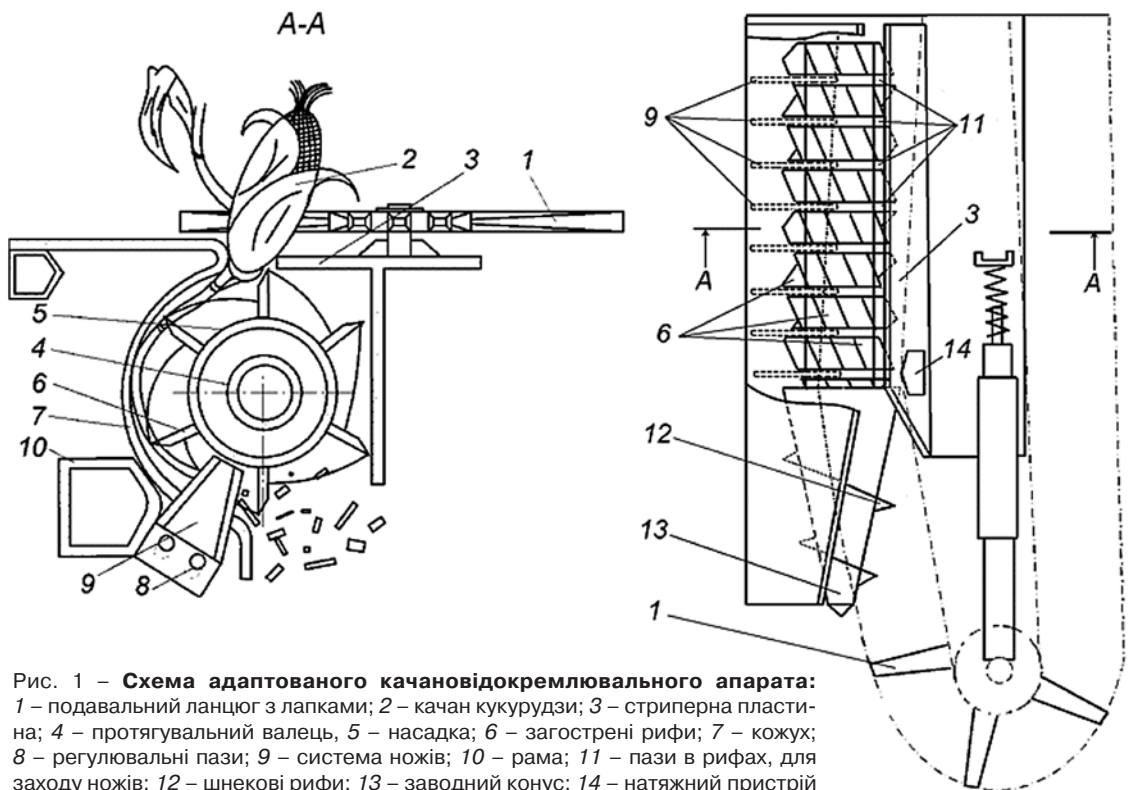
Схема адаптованого качановідокремлювального апарата: 1 – подавальний ланцюг з лапками; 2 – качан кукурудзи; 3 – стріперна пластина; 4 – протягувальний валець; 5 – насадка; 6 – загострені рифи; 7 – кожух; 8 – регульовальні пази; 9 – система ножів; 10 – рама; 11 – пази в рифах, для заходу ножів; 12 – шнекові рифи; 13 – заводний конус; 14 – натяжний пристрій
